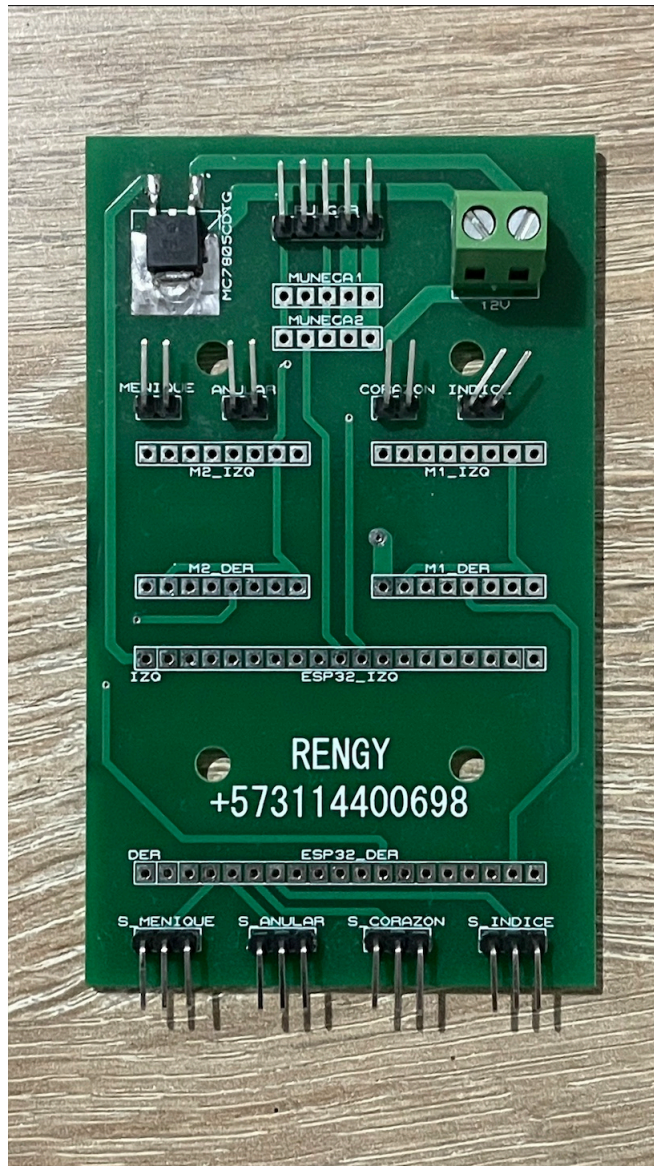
Error de diseño primer prototipo placa PCB.
